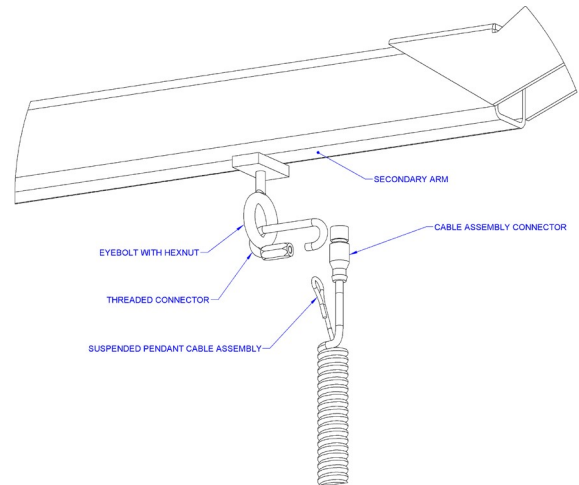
C1. Assemblaggio del gruppo del cavo sospeso nella parte inferiore del gruppo azionatore.
